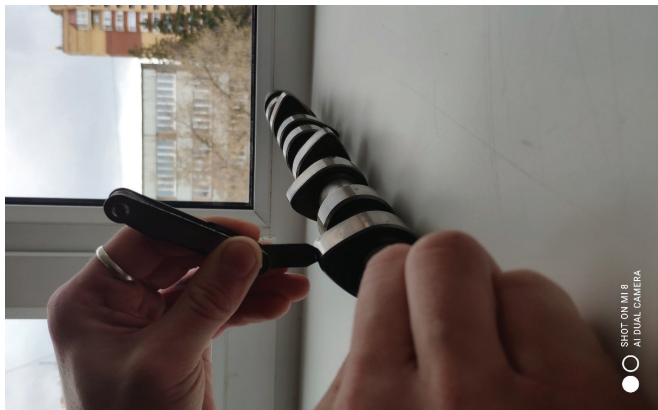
Профиль кулачка впускного клапана двигателя ВАЗ 21111:
